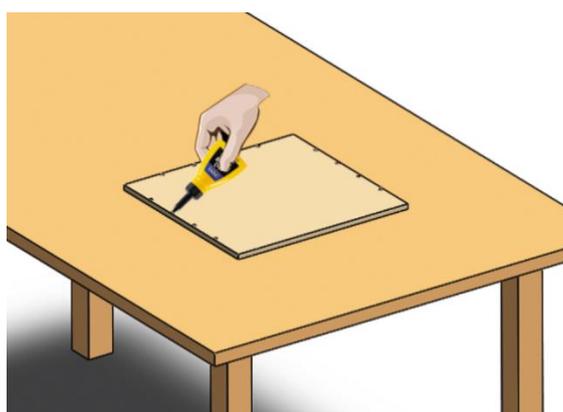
Paso 5 del ensamblaje del cajón (conjunto 2)
